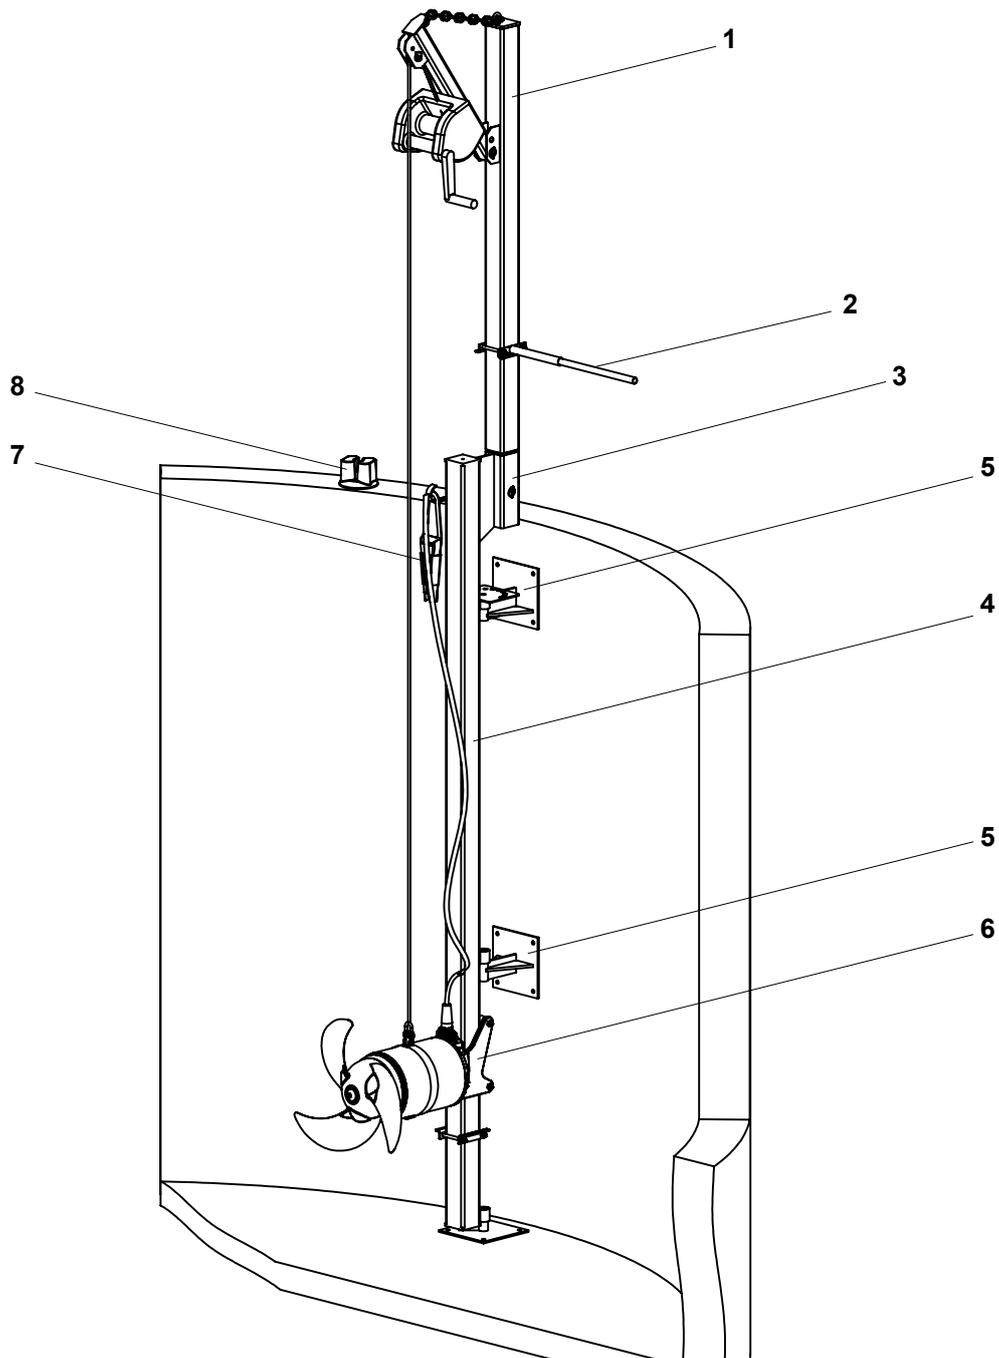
Exemple d'installation avec d'autres possibilités de fixation
